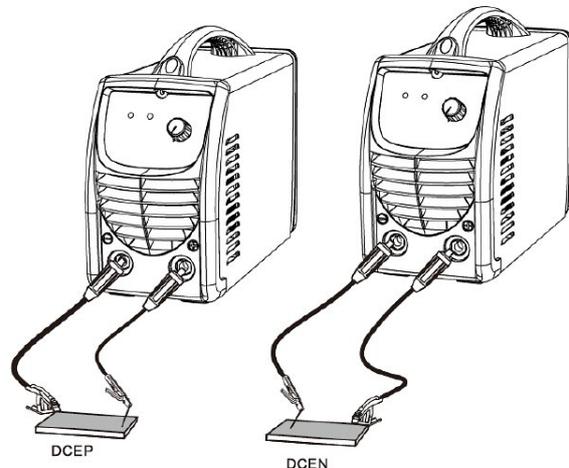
Anschluss für Lichtbogenhandschweißen
